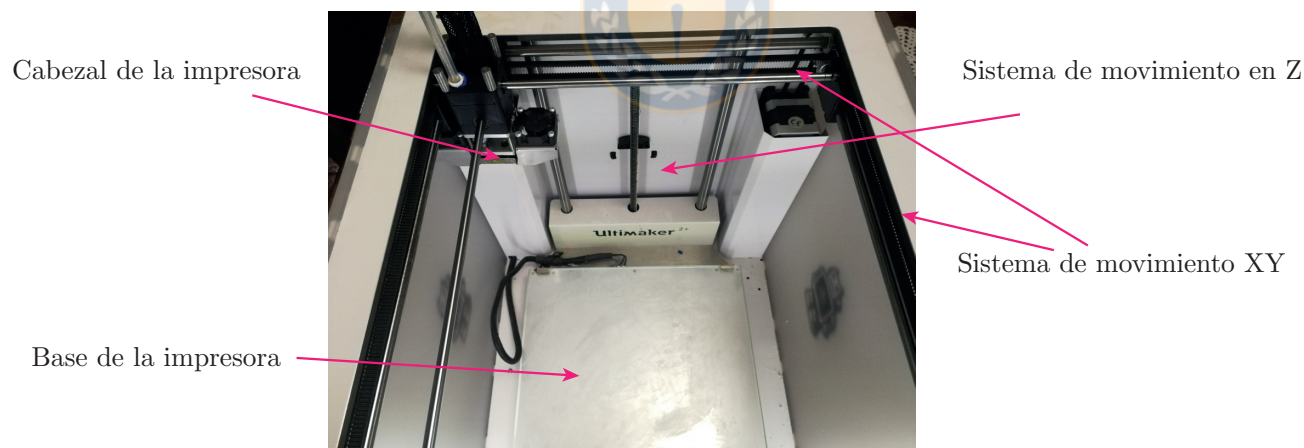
Partes más importantes de una impresora 3D. Foto de la impresora Ultimaker s2⁺.
